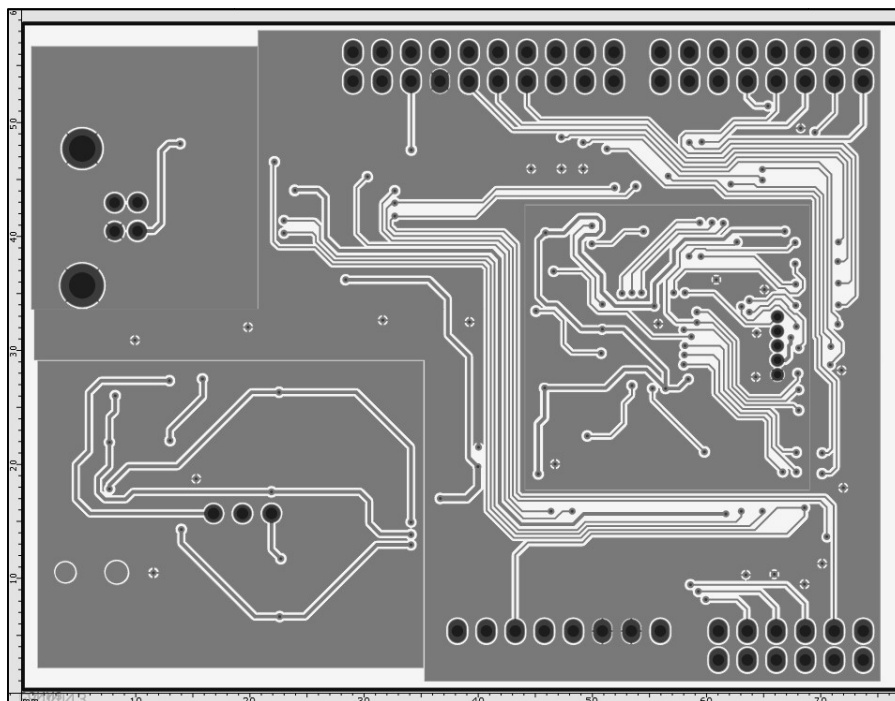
Módulo PCB fusionado: cara BOTTOM
